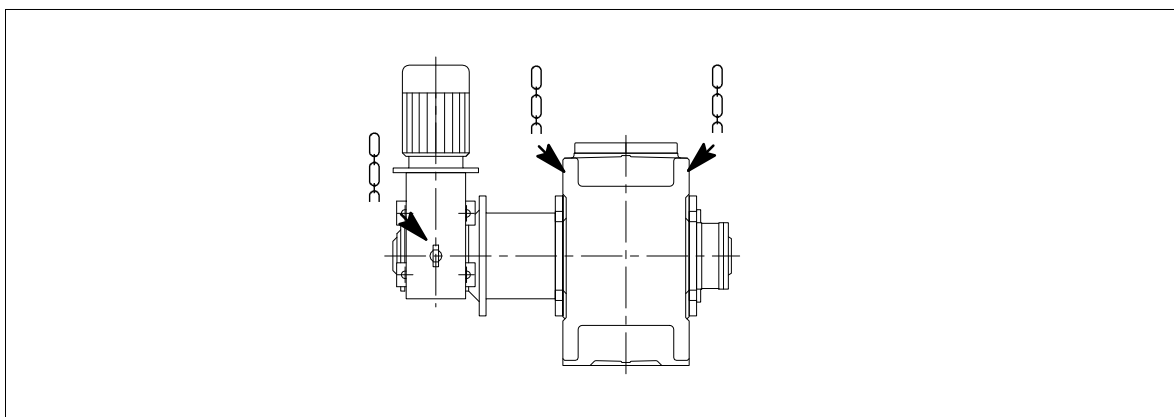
Body pro uvázání na převodkách typů H... s motorem
